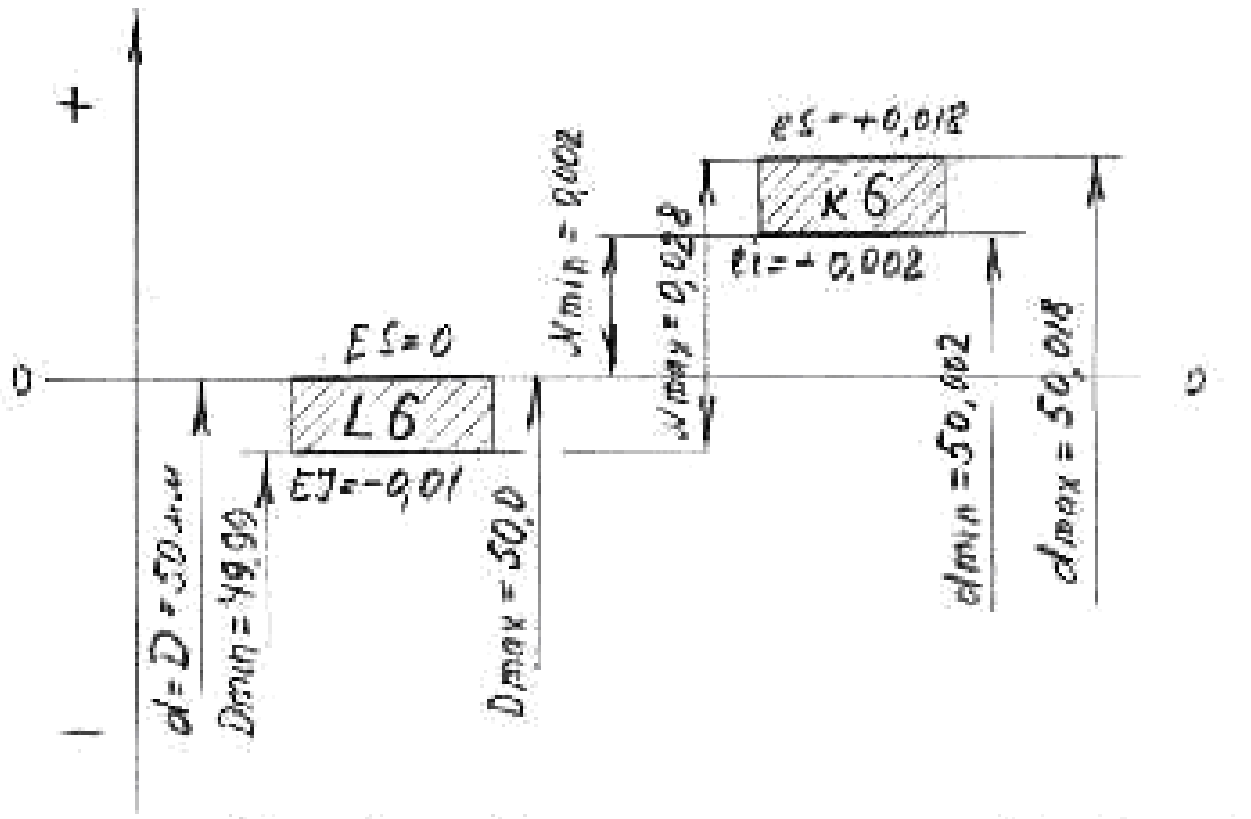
Графическая схема полей допусков посадки внутреннего кольца подшипника на вал
